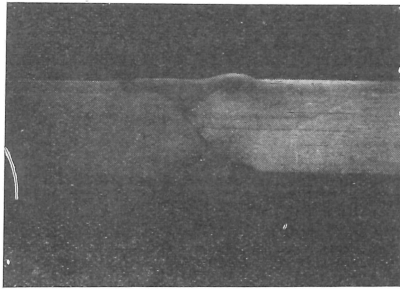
Coupe transversale dans la soudure représentée figure 9a.
